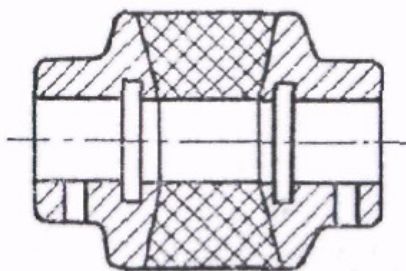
Конструкция типовой резинометаллической муфты
